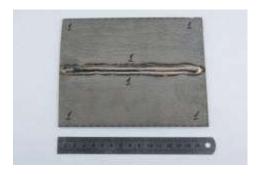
Общий вид образца из сплава Ti-6Al-4Zr-2Sn-Nb-0.6Mo после сварки
